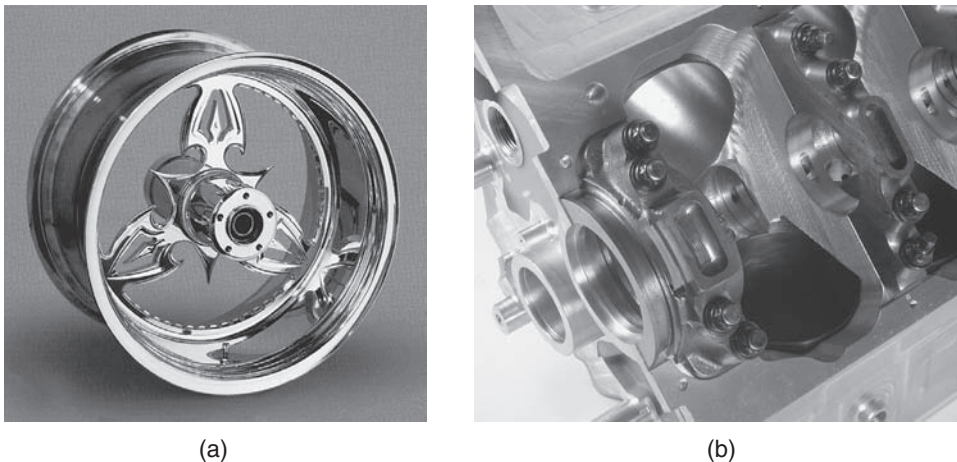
Ejemplos de partes que se pueden mecanizar en centros de maquinado mediante diversos procesos como torneado, careado, fresado, taladrado, mandrinado, rimado y roscado. Es común que dichas partes requieran el uso de varias máquinas herramienta para concluir las. (a) Rueda forjada de motocicleta, maquinada de acabado para obtener la tolerancia, y posteriormente pulida y recubierta. (b) Vista detallada de un monobloque de motor, que muestra cavidades complejas, orificios roscados y superficies planas. Fuente: (a) Cortesía de R. C. Components. (b) Cortesía de Donovan Engineering, programación por Norman Woodruff y fotografía de Ed Dellis, Powersports photography.
